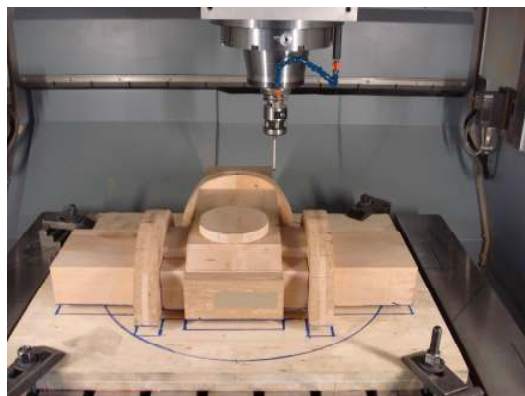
Test programu v ručním režimu zobrazení ve 3D
